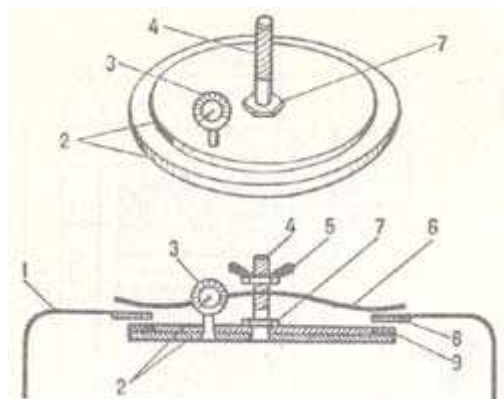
Самодельная крышка, к сковородке: 1 — сковорода; 2 — крышка (из двух пластин или выточенная); 3—манометр; 4 — винт; 5 — барашек; 6 — фигурная пластина; 7 — прижимная гайка; 8 — кольцо усиления; 9 — резиновое кольцо.
